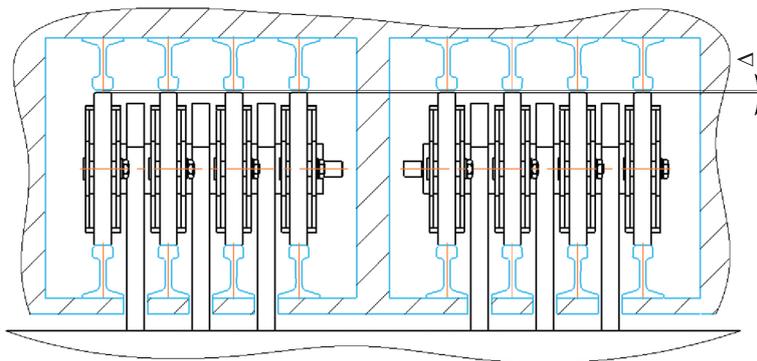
Общий вид роликового ползуна — узла сопряжения ТУТ с подъемно-установочным агрегатом
